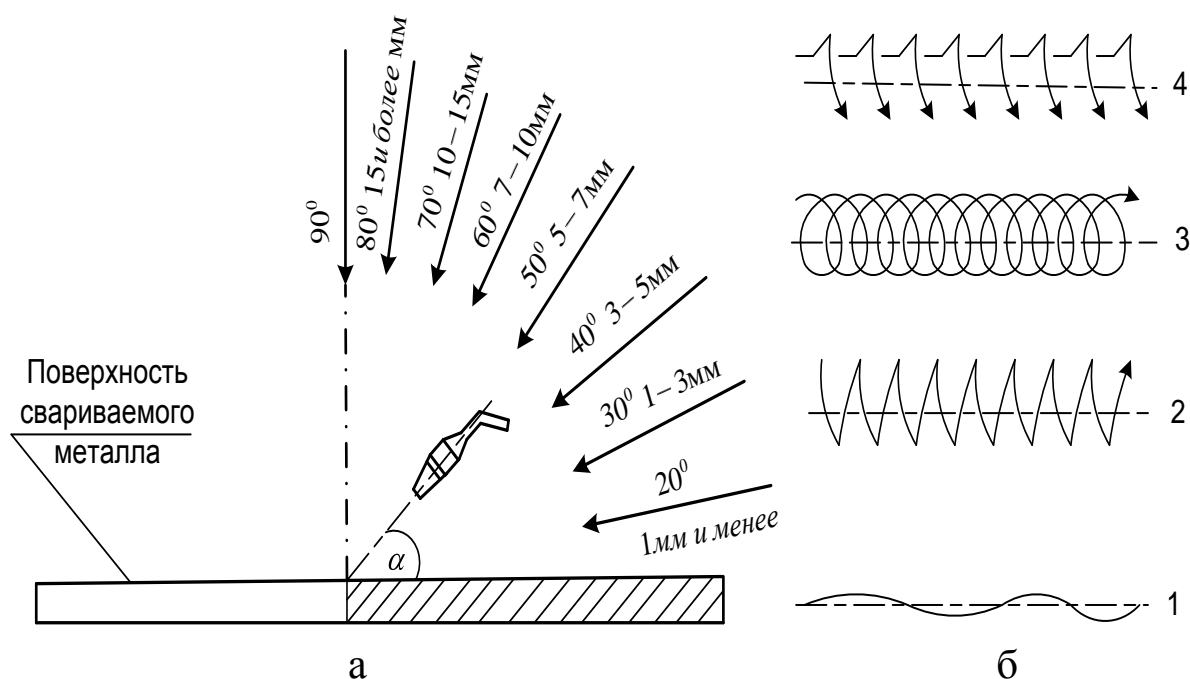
Углы наклона мундштука горелки при сварке различных толщин (а) и способы перемещения мундштука горелки (б):
